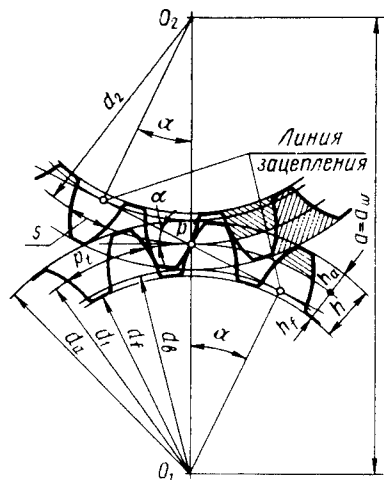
Схема зацепления прямозубых цилиндрических колес
